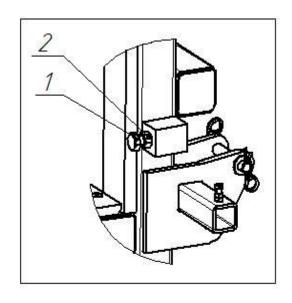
Регулировка угла выдвинутого положения рычага бокового
